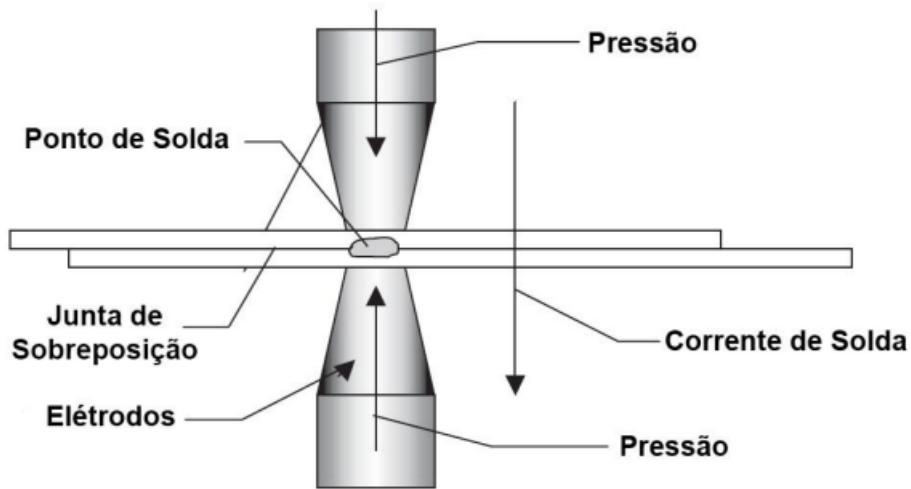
Soldadura por pontos. Fonte: [9]
